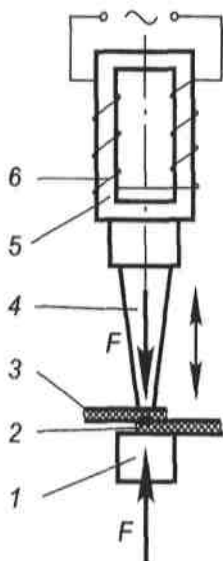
Схема ультразвукового зварювання: 1 – опора; 2, 3 – заготовка; 4 – хвилевід; 5 – вібратор; 6 – обмотка; F – сила
